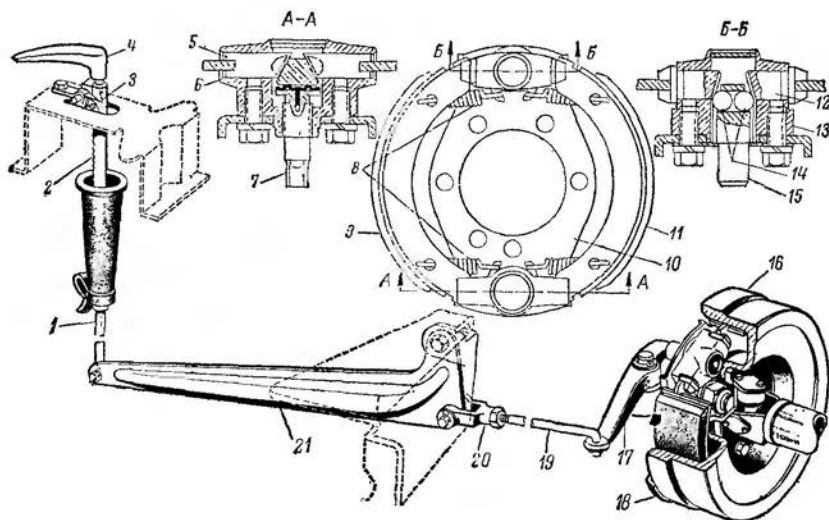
Ручной тормоз автомобиля ГАЗ-66 и его привод:
